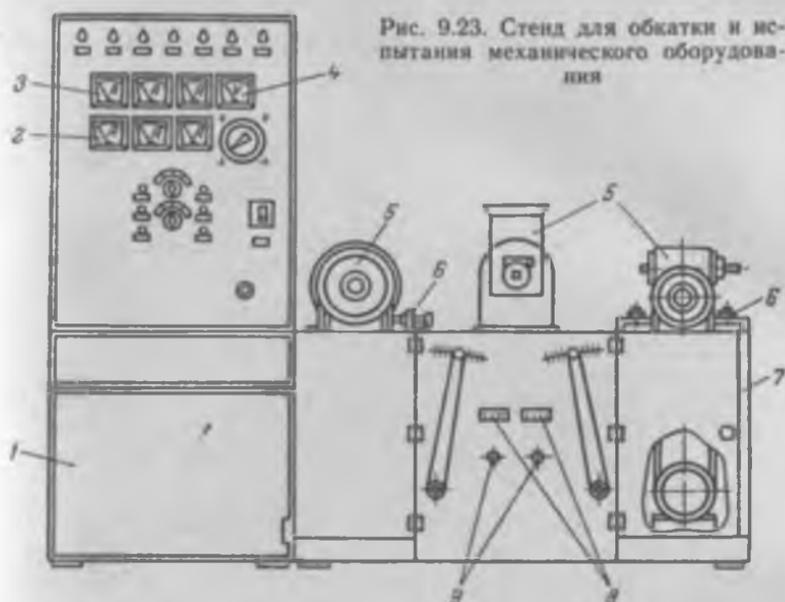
Стенд для обкатки и испытания механического оборудования
